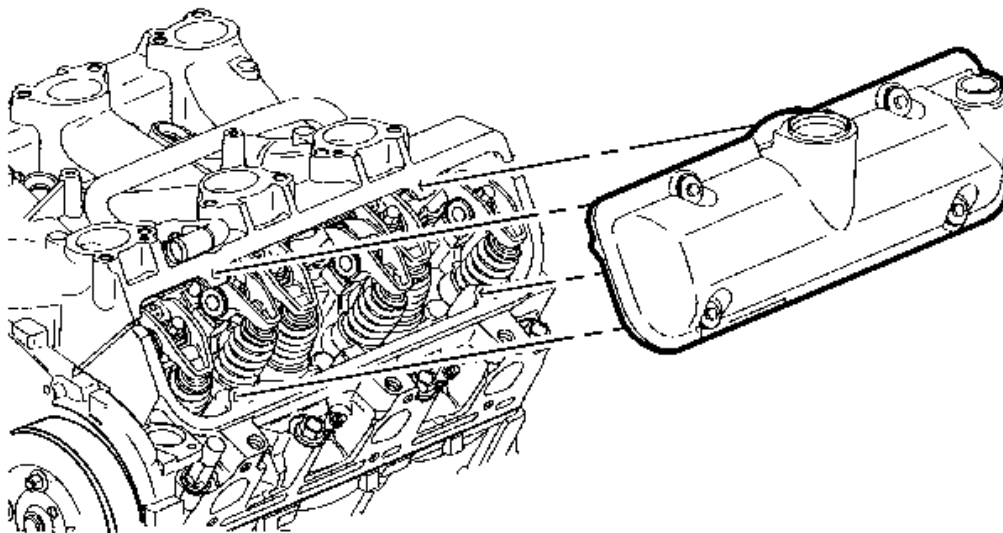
Vista de la cubierta del balancín de válvulas - Izquierda
